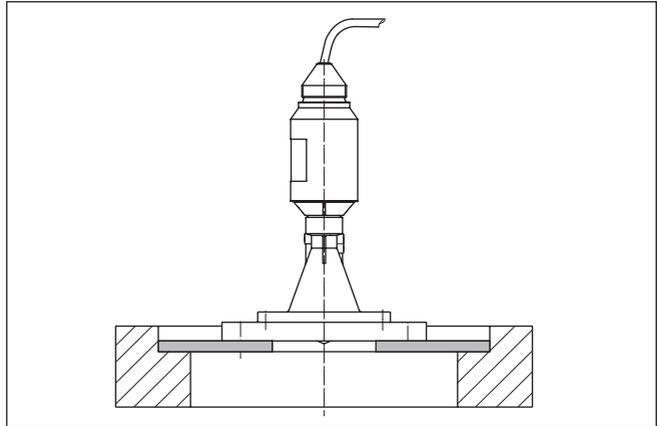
Montage mittels des Adapterflansches, z. B. auf einer Schachtabdeckung.
